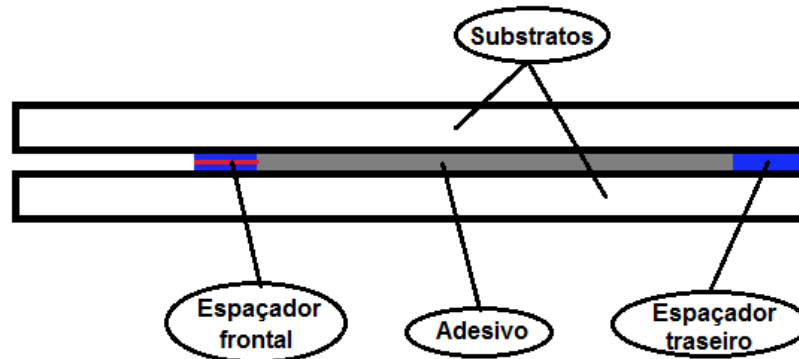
Esquema de colocação de espaçadores para provetes DCB e ENF [3].
